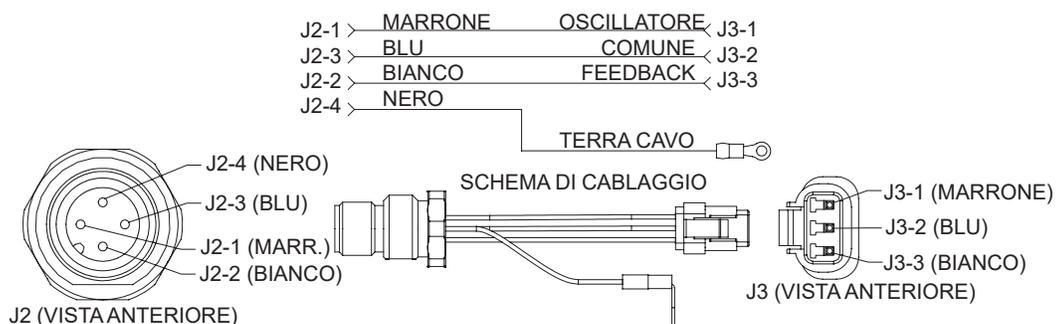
Cablaggio dell'alloggiamento della pistola a spruzzo
